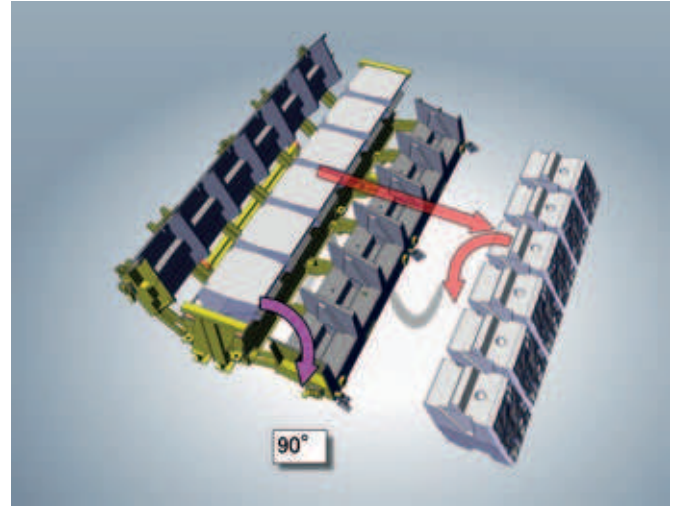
'de Furusato markasını taşıyan beton eleman, bentlerde kullanılan bir taş istinat duvarını göstermektedir. Bu duvarlar, betondan imal edilmiş bir takviye çubuğu üzerinde 6 adet ayrı blok parçasından oluşmaktadır. Böylesine karmaşık bir ürün sadece ayrıntılı bir şekilde planlanmış bir kalıp içinde betonlanarak üretilmektedir. Kalıbın özel tasarımı, 6 ayrı bloğun tek bir kalıp içinde betonlanmasını sağlamaktadır. Şekil 9 ve 10'da kalıpların el aletleri yardımıyla kolayca kullanılabildiği görülmektedir. Dış kalıp, sıyırma işlemi için 90
